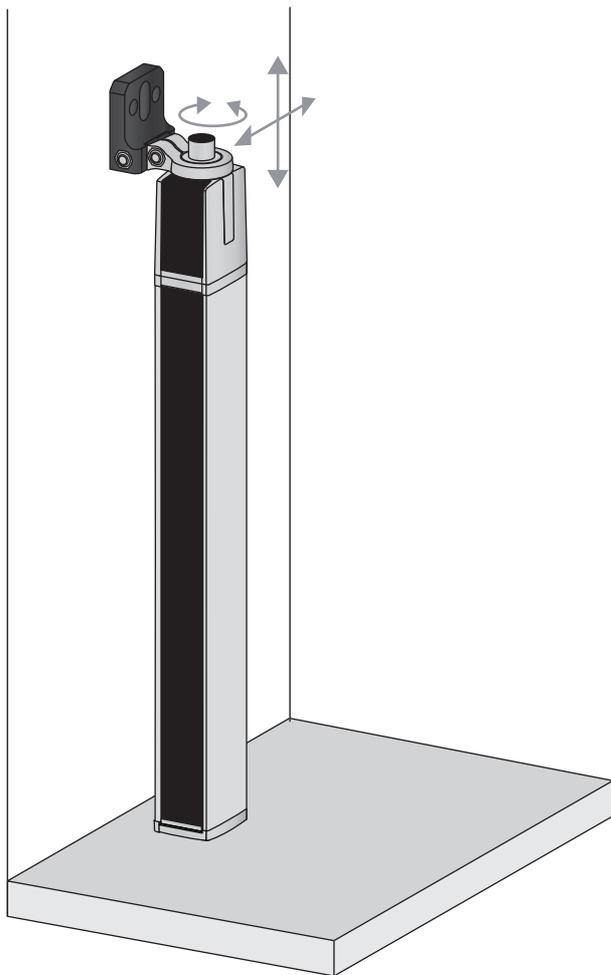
Befestigung direkt auf dem Maschinentisch
